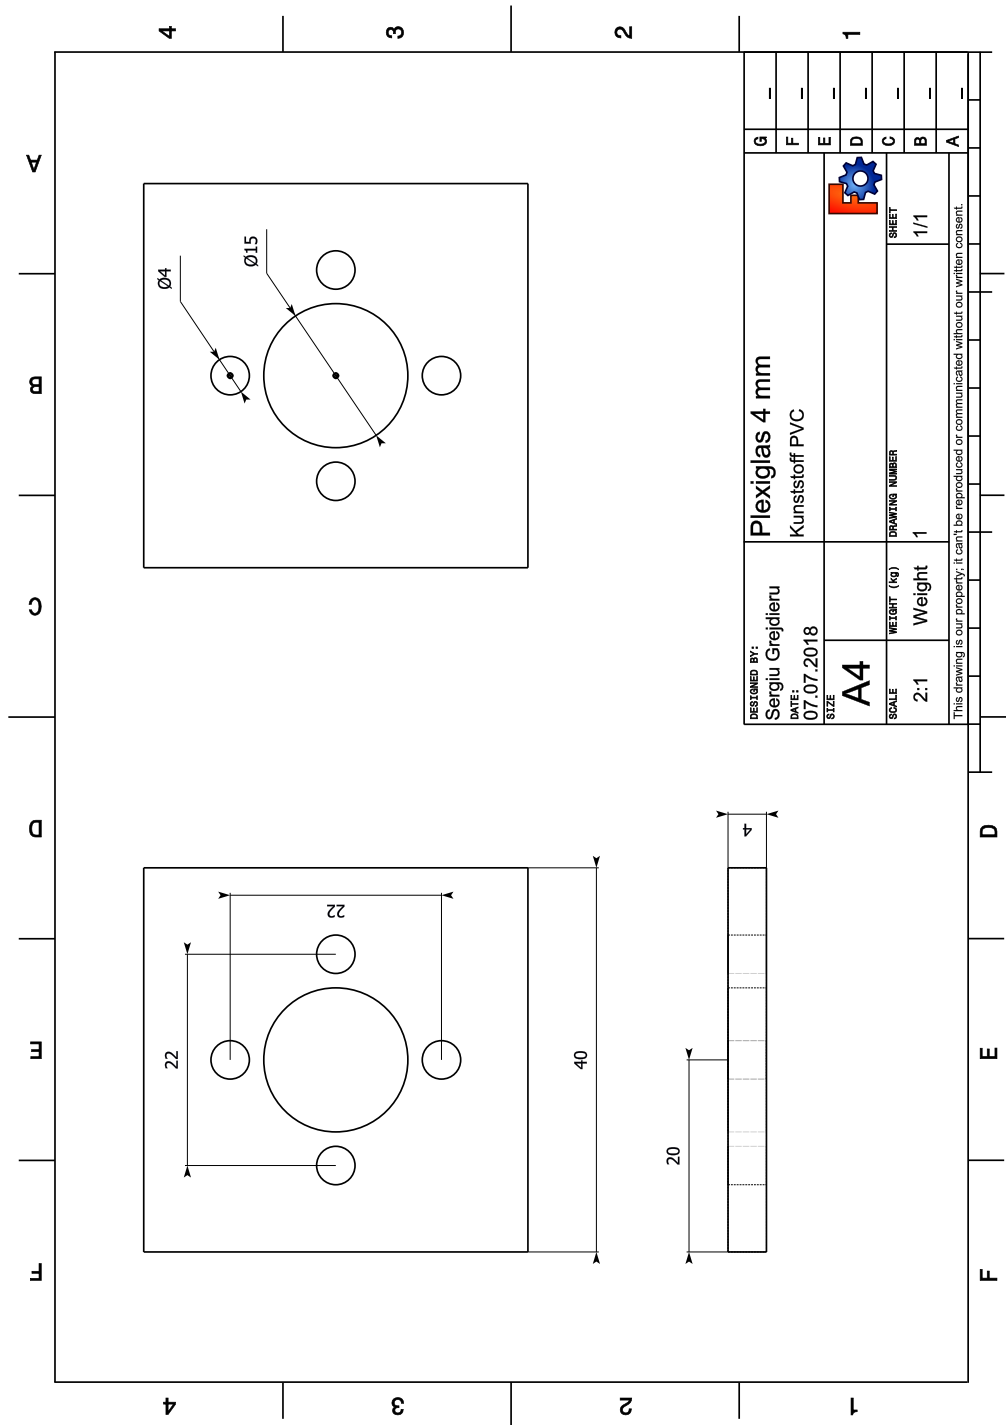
Technische Zeichnung: Plexiglass mit 4 mm Dicke
